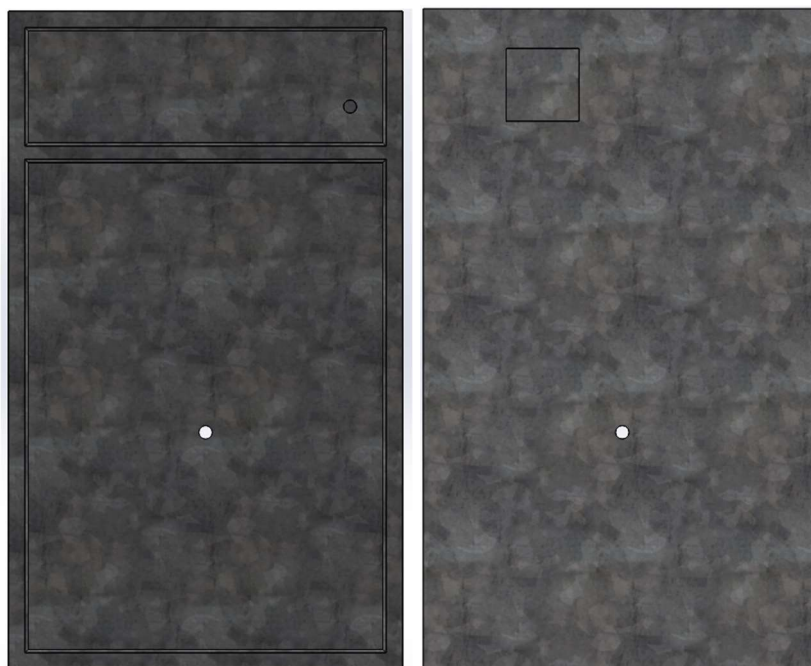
Vista frontal (izquierda) y vista posterior (derecha) de la carcasa externa.
